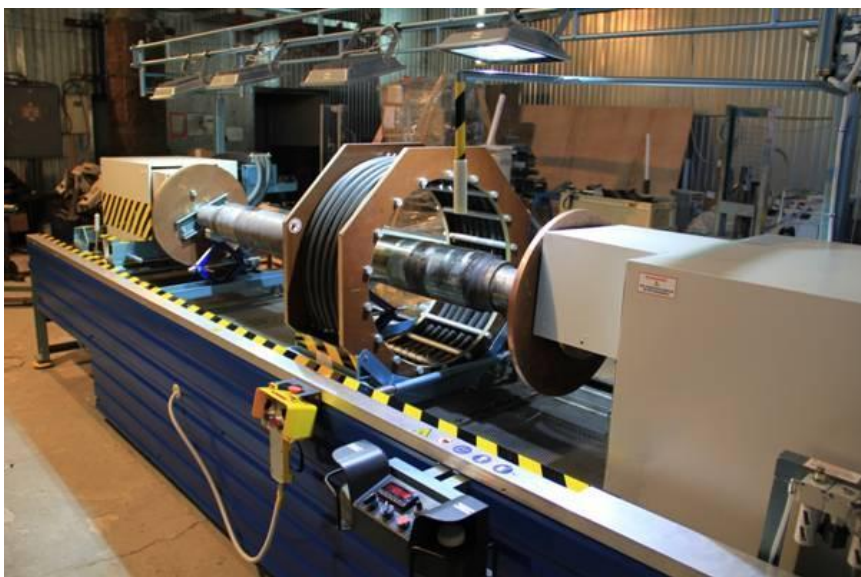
Стенд магнітопорошкового контролю великогабаритних деталей УМПК-39
